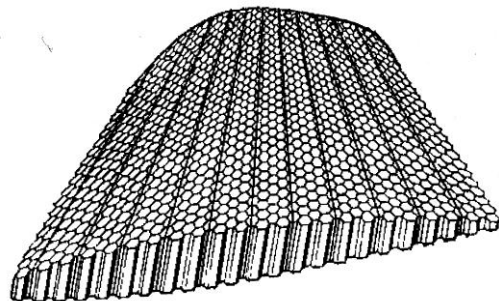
Сотовый заполнитель, фрезерованный по копиру
